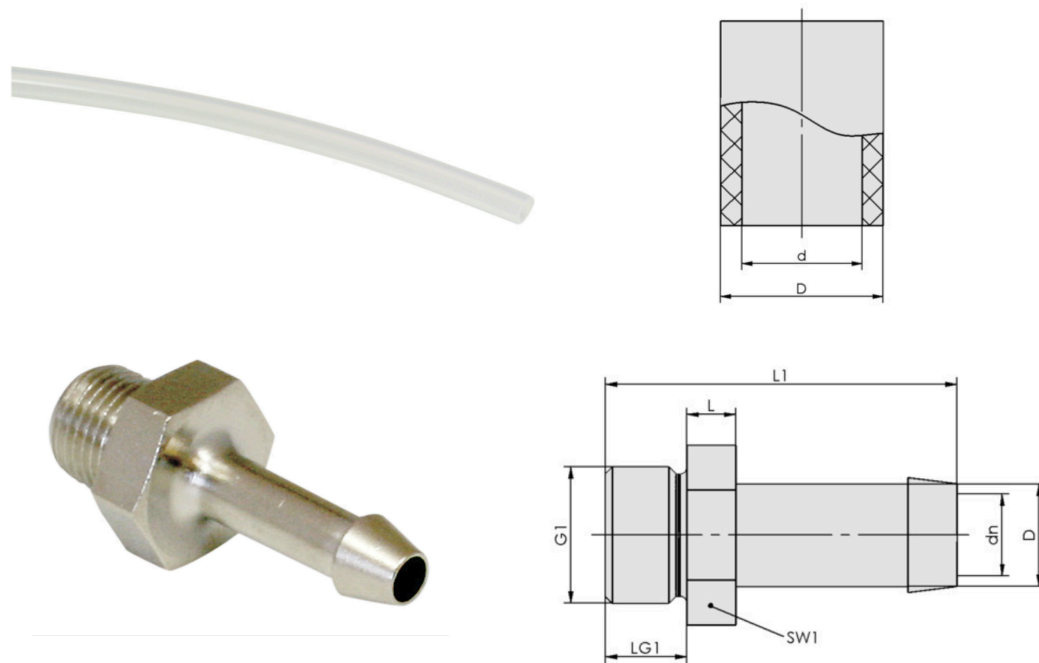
imagen y cotas de dimensiones de tubos flexibles con boquillas del fabricante Schmalz. Fuente: Schmalz.
